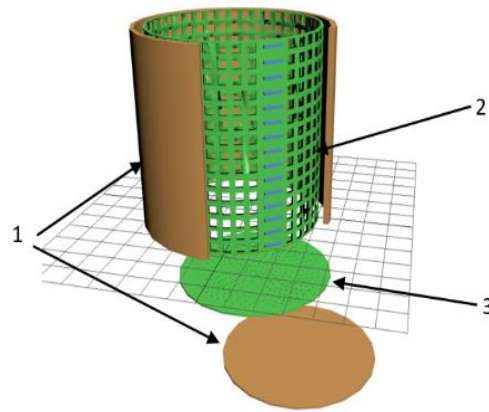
Конструкция форм для заливки образцов: 1 – мешковина; 2 – перфорированный материал с габаритами ячейки 3x3 мм; 3 – перфорированный материал с габаритами ячейки 1x1 мм
